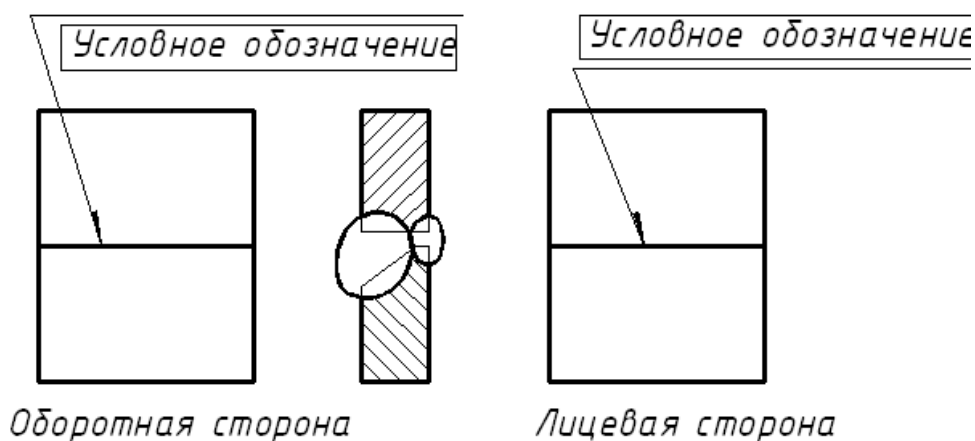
Обозначение сварного шва с лицевой и оборотной стороны
